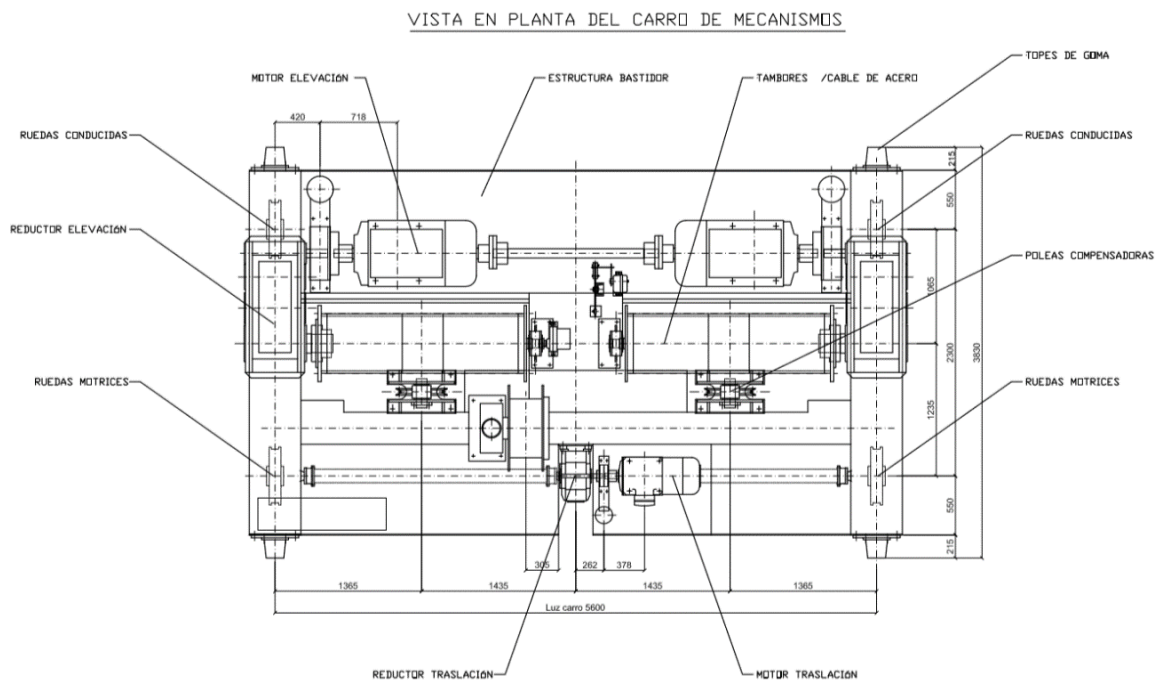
nº1. Vista en planta de los componentes del carro. (Fuente: David Ventura)
